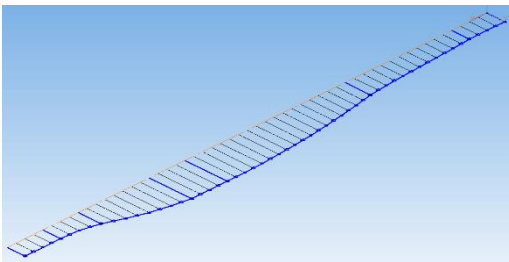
Ескіз розрахованого контуру робочої поверхні резонаторної труби
